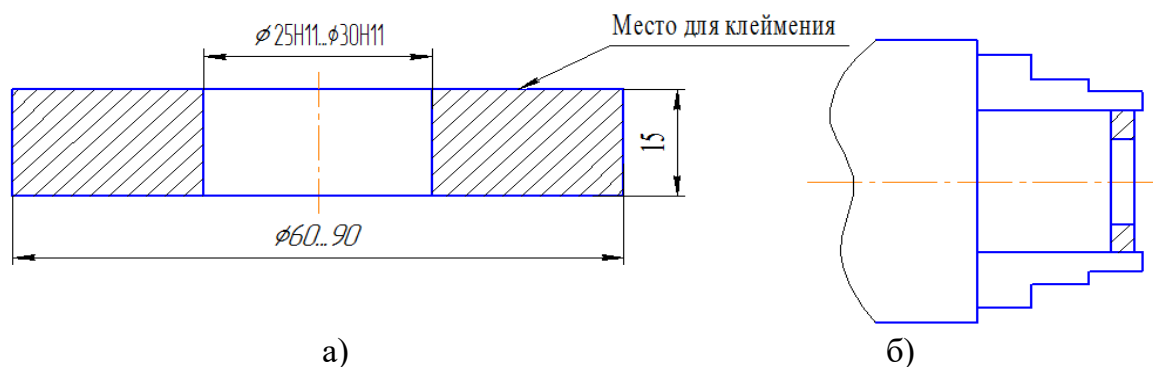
Заготовка (а) и схема закрепления ее в патроне (б)
